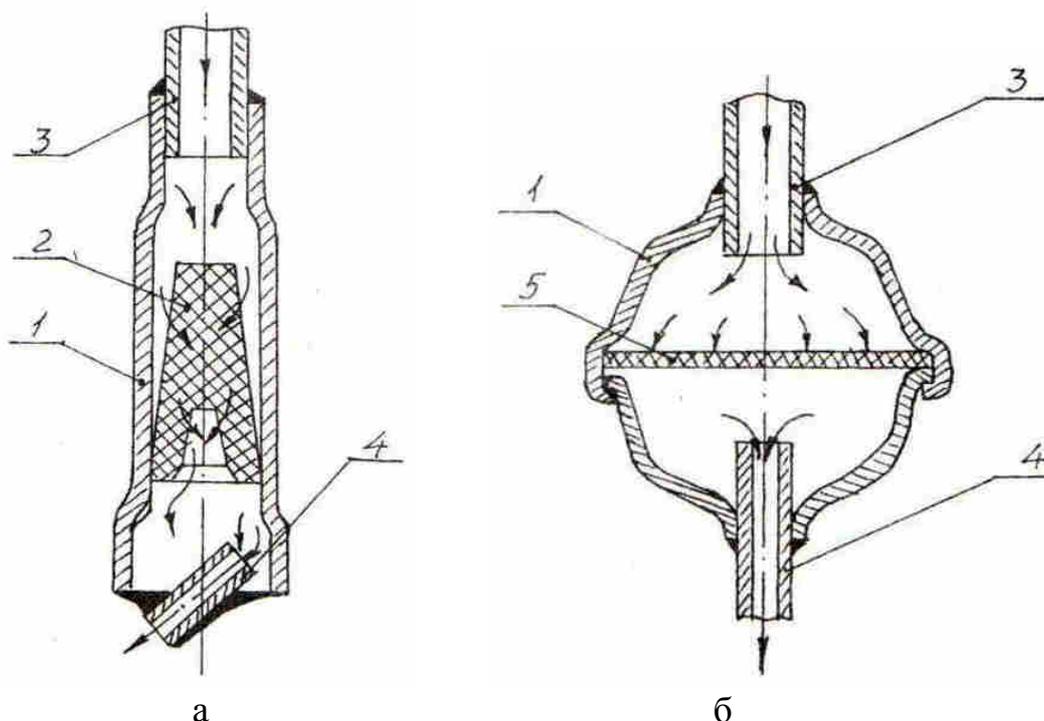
Фильтры капиллярные: а – металлокерамический; б – сетчатый; 1 - корпус; 2 - фильтр; 3 - трубка конденсатора; 4 - капиллярная трубка; 5-фильтрующая сетка
